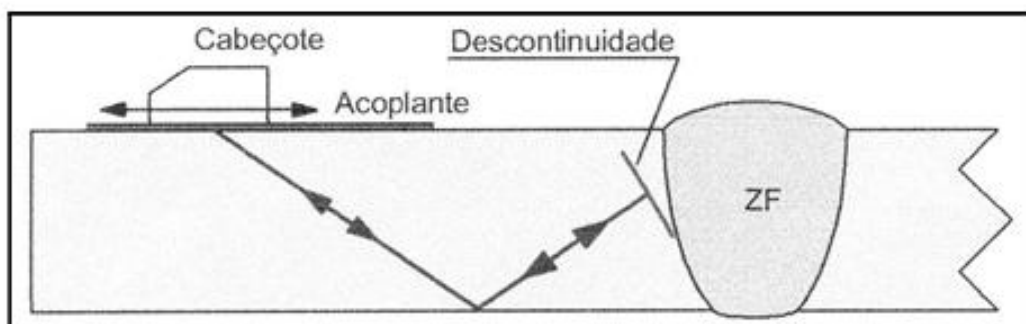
Inspeção ultra-sônica de uma junta soldada com cabeçote angular.
